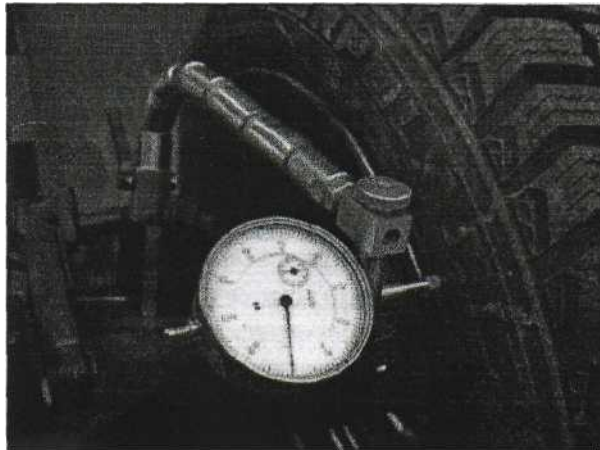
Установка индикатора для измерения бокового биения шины
